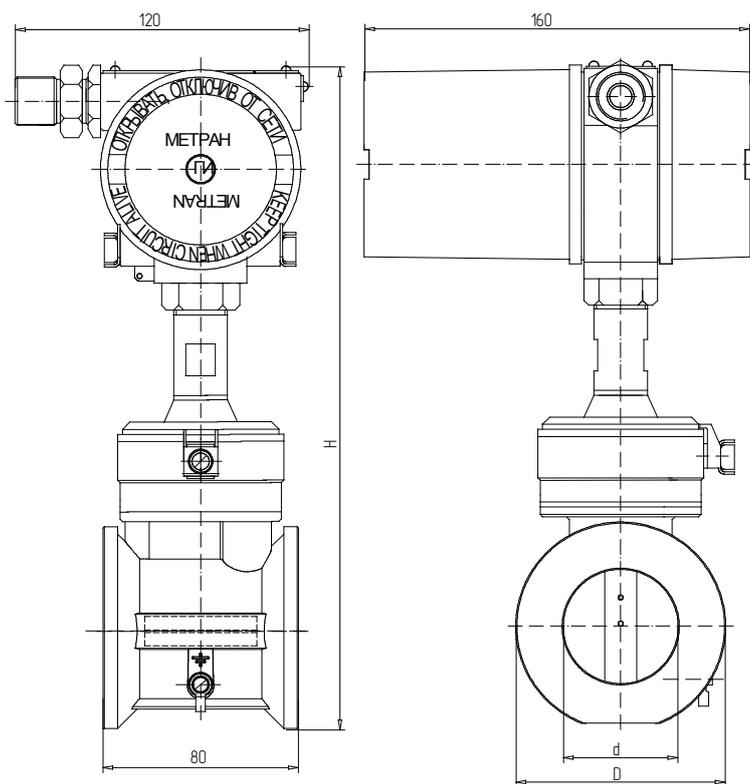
Общий вид датчика Ду50, Ду80
